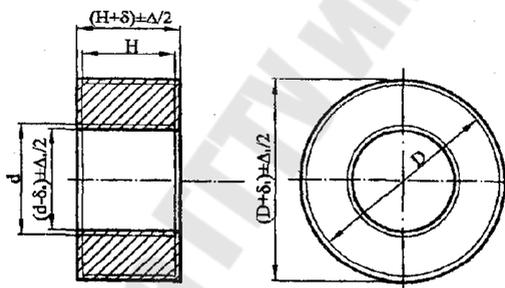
Схема назначения припусков и допусков для поковок 3-й группы
